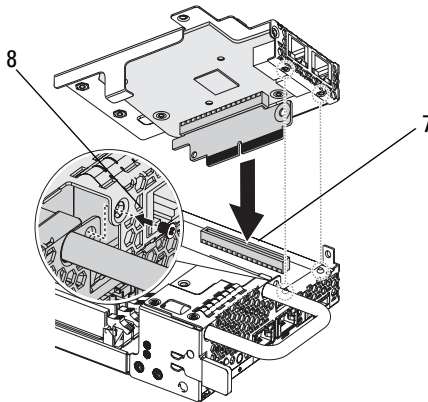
Installation d'un assemblage mezzanine sur un chariot
